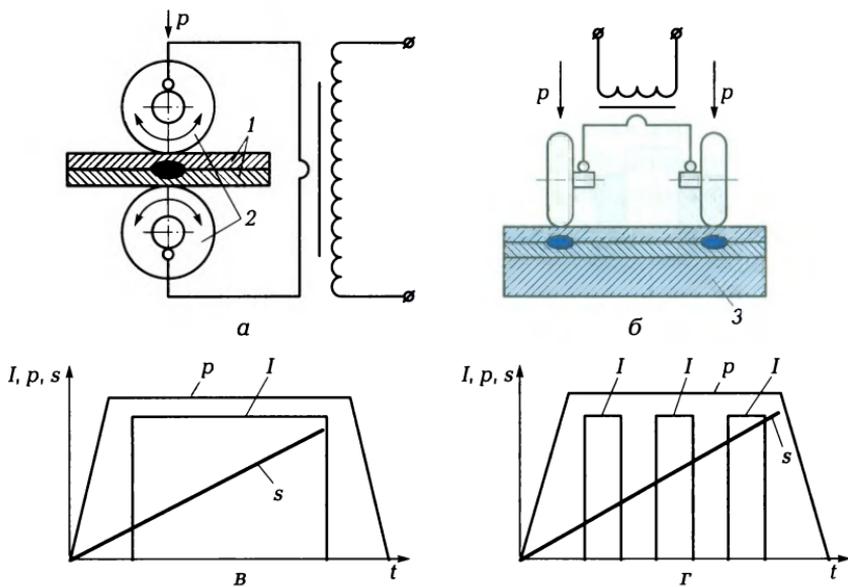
Схемы двухсторонней (а) и односторонней (б) шовной сварки; циклограммы процесса шовной сварки с непрерывным (в) и с прерывистым (г) включением тока:
